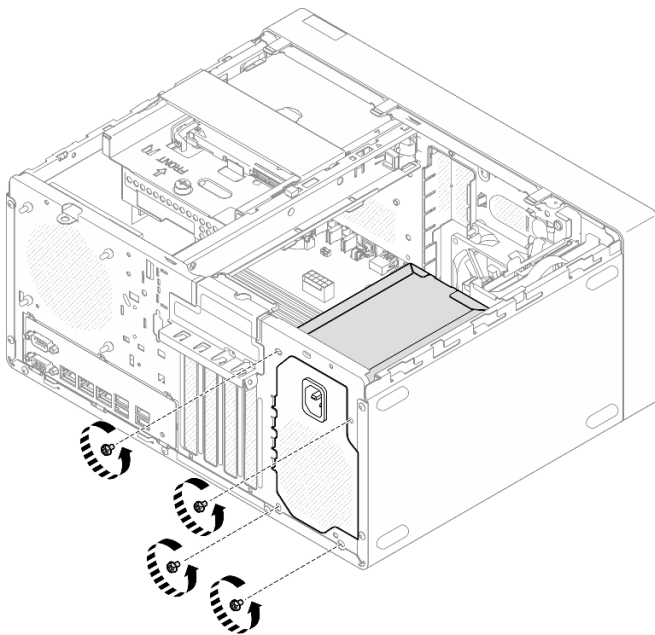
Entfernen der Schrauben, mit denen die Netzteilereinheit am Gehäuse befestigt ist
